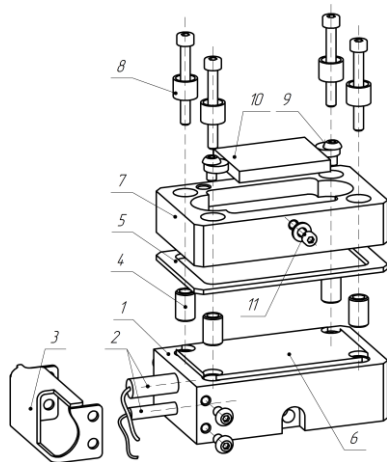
Схема ванночки: 1 – Основание; 2 – Термопара; 3 – Кожух защитный ; 4 – Изолятор; 5 – Прокладка-изолятор; 6 – Термопаста; 7 – Ванночка; 8 – Изолятор; 9 – Подшипник эксцентриковый; 10 – Образец; 11 – Клемма присоединительная.
